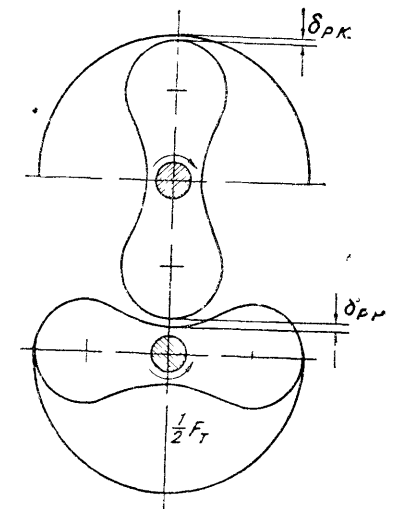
Схема роторного механизма для определения поверхностей, подвергающихся попеременно воздействию высокого и низкого давления.
